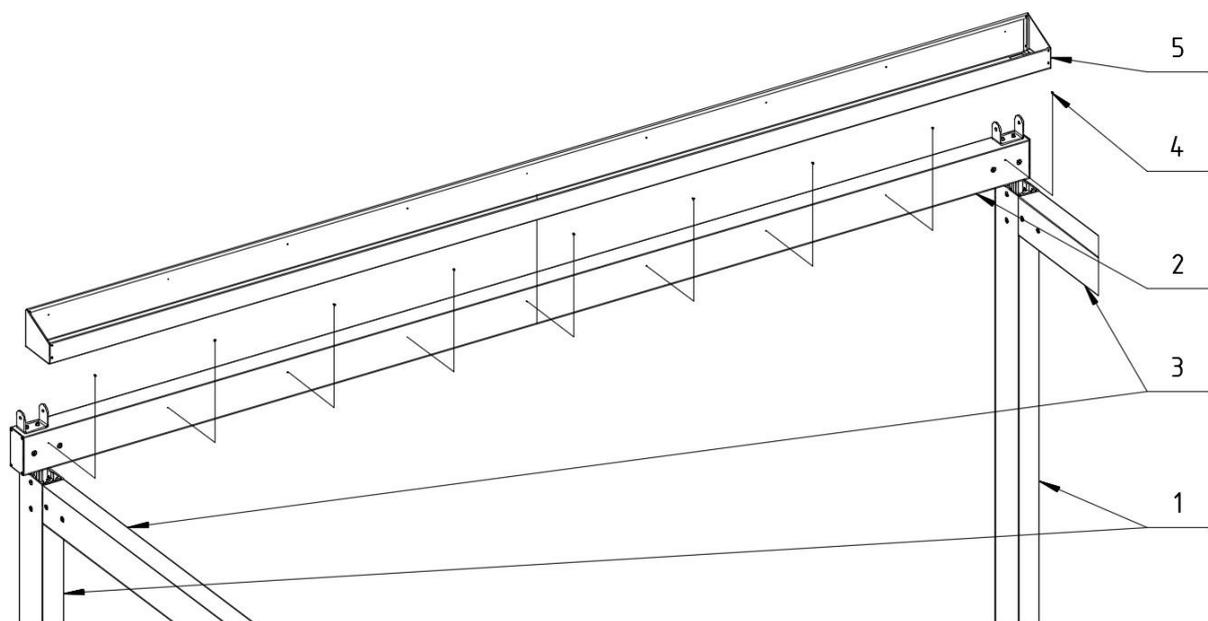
Assemblage de la gouttière : 1 - Poteau bas, 2 - Poutre avant, 3 Poutre latérale, 4 - Vis autoperceuses St 2,9x6,5 , 5 - Gouttière.
